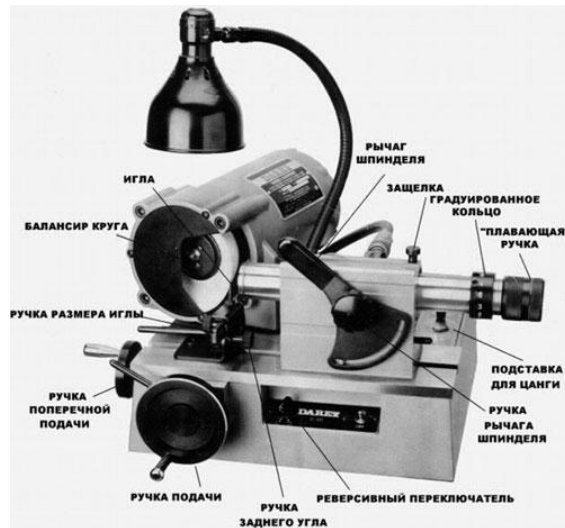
Спеціальний верстат для заточки фрези [3]
